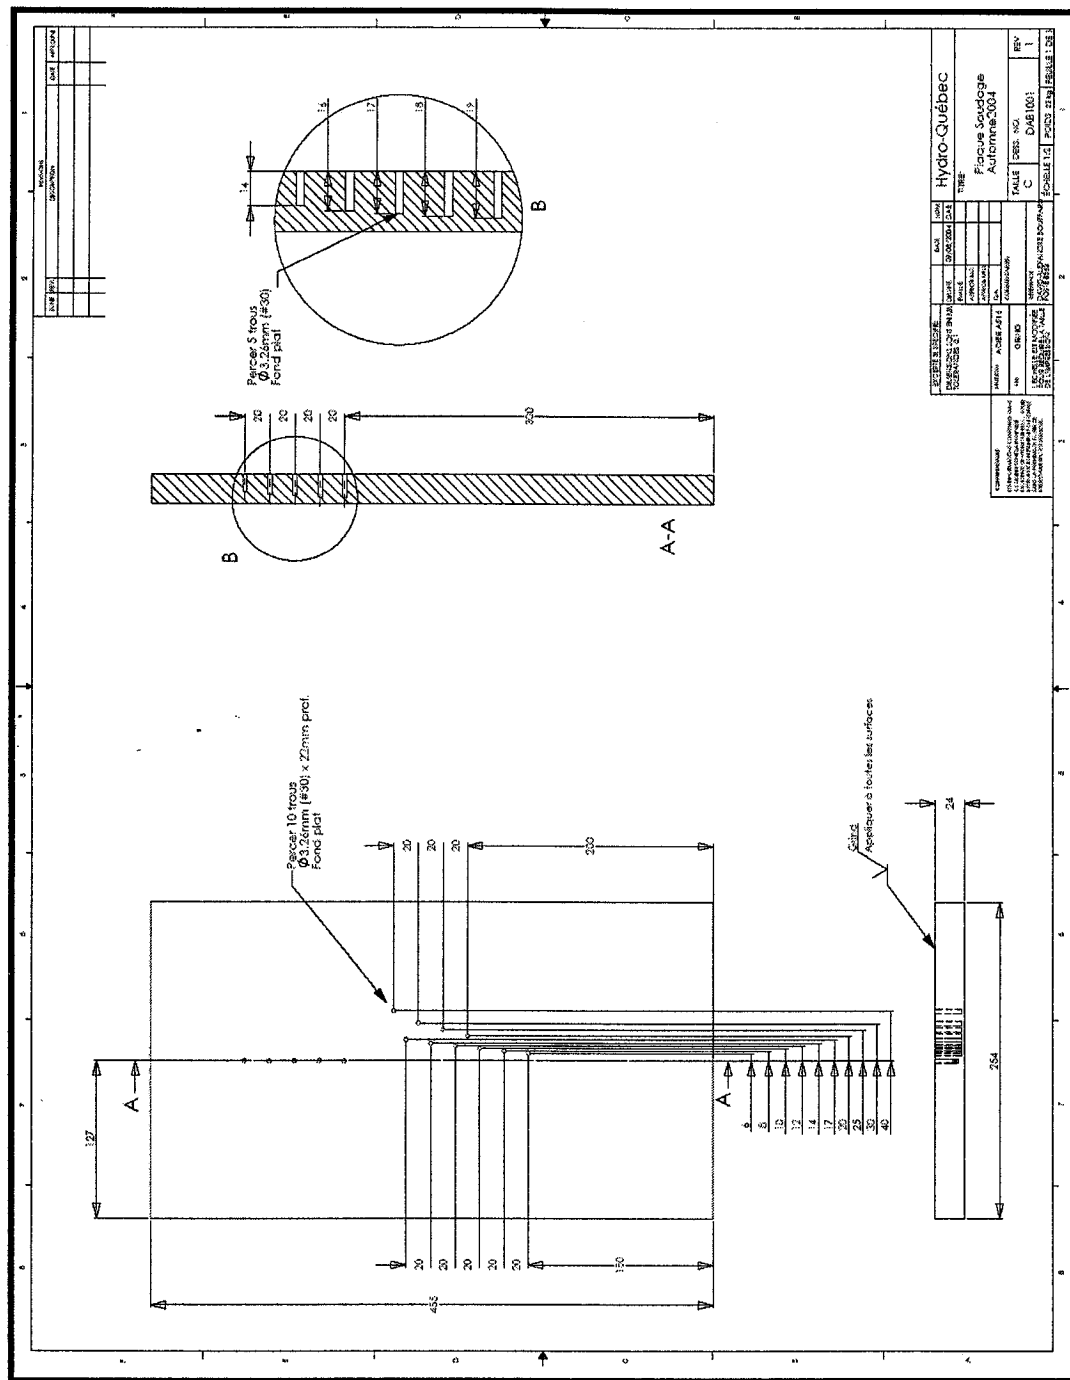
Dessin d'usinage indiquant la position des thermocouples sur la plaque d'acier ASTM A516
